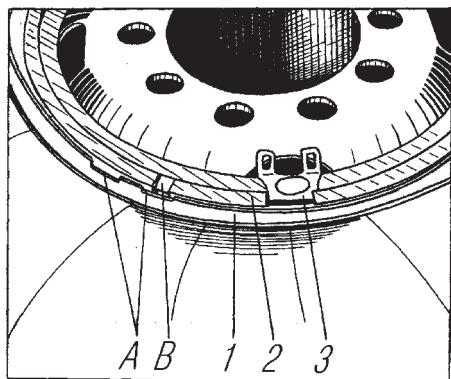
Положение замочного и бортового колец колес 254Г-508 и 400Г-508:
